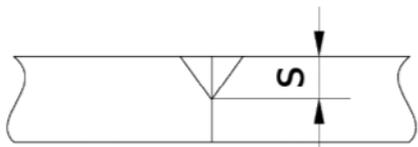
Profundidad del cordón en soldadura a tope
